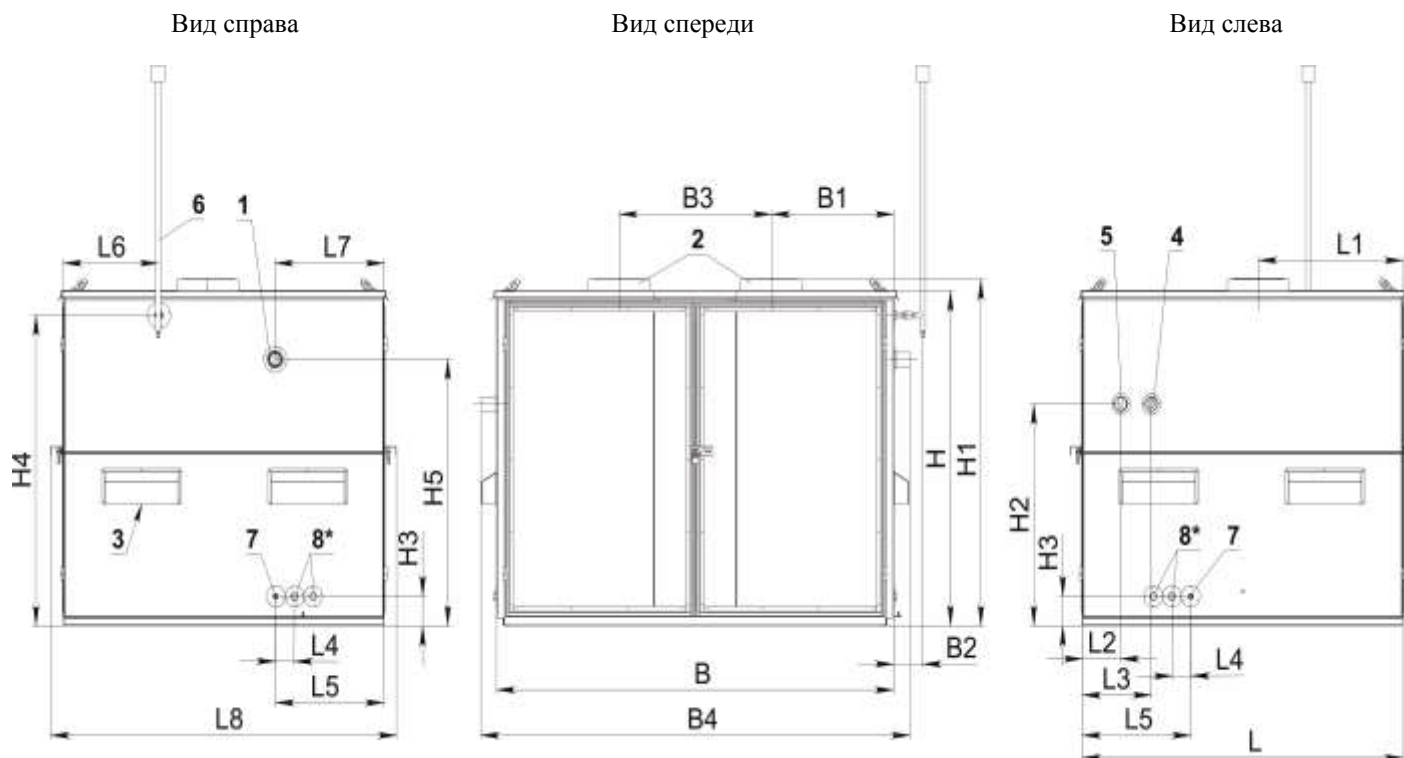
Габаритно-присоединительные размеры котла RSH500, RSH600, RSH800
